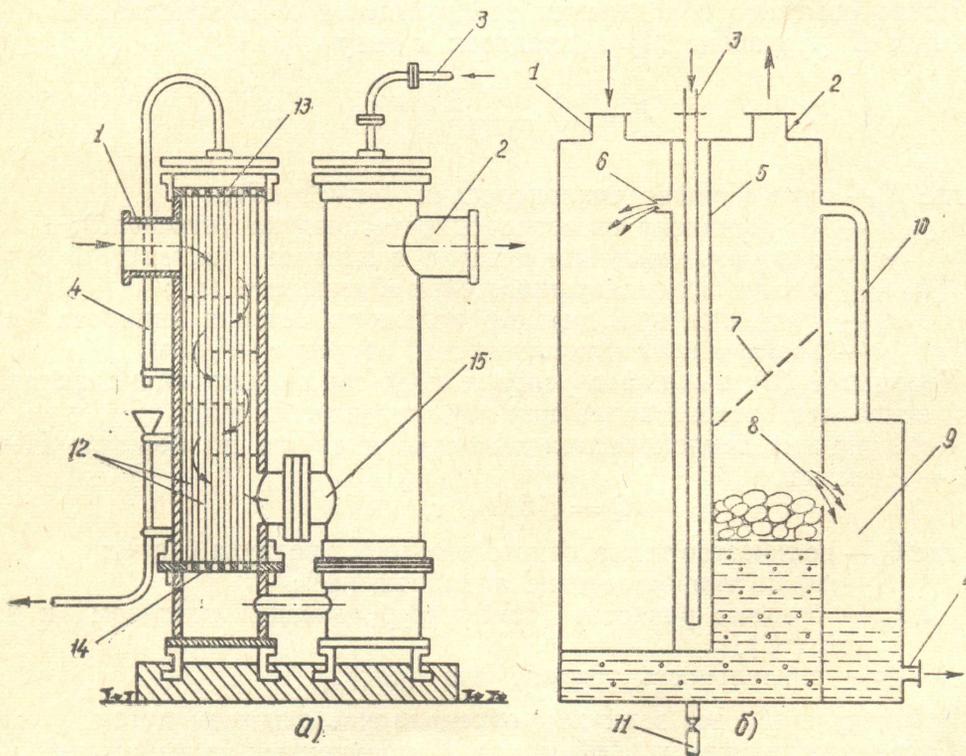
Конструктивные схемы аппаратов для охлаждения сжатого воздуха в компрессорах
